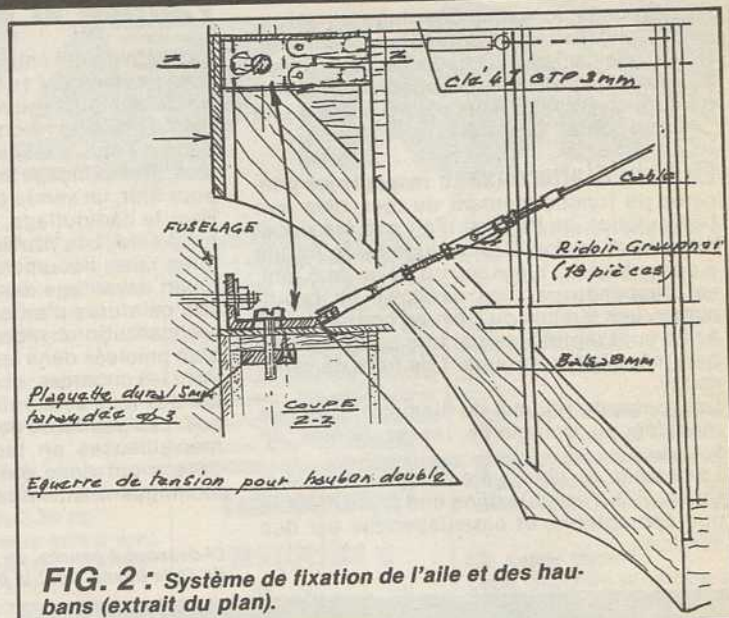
Système de fixation de l'aile et des haubans (extrait du plan).
